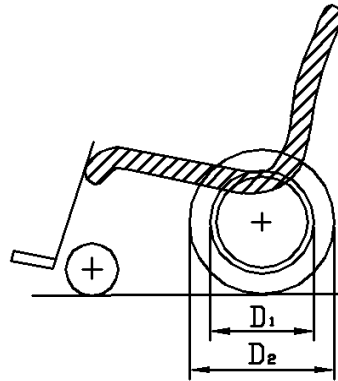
Диаметр ручного приводного обода и диаметр ведущего колеса
